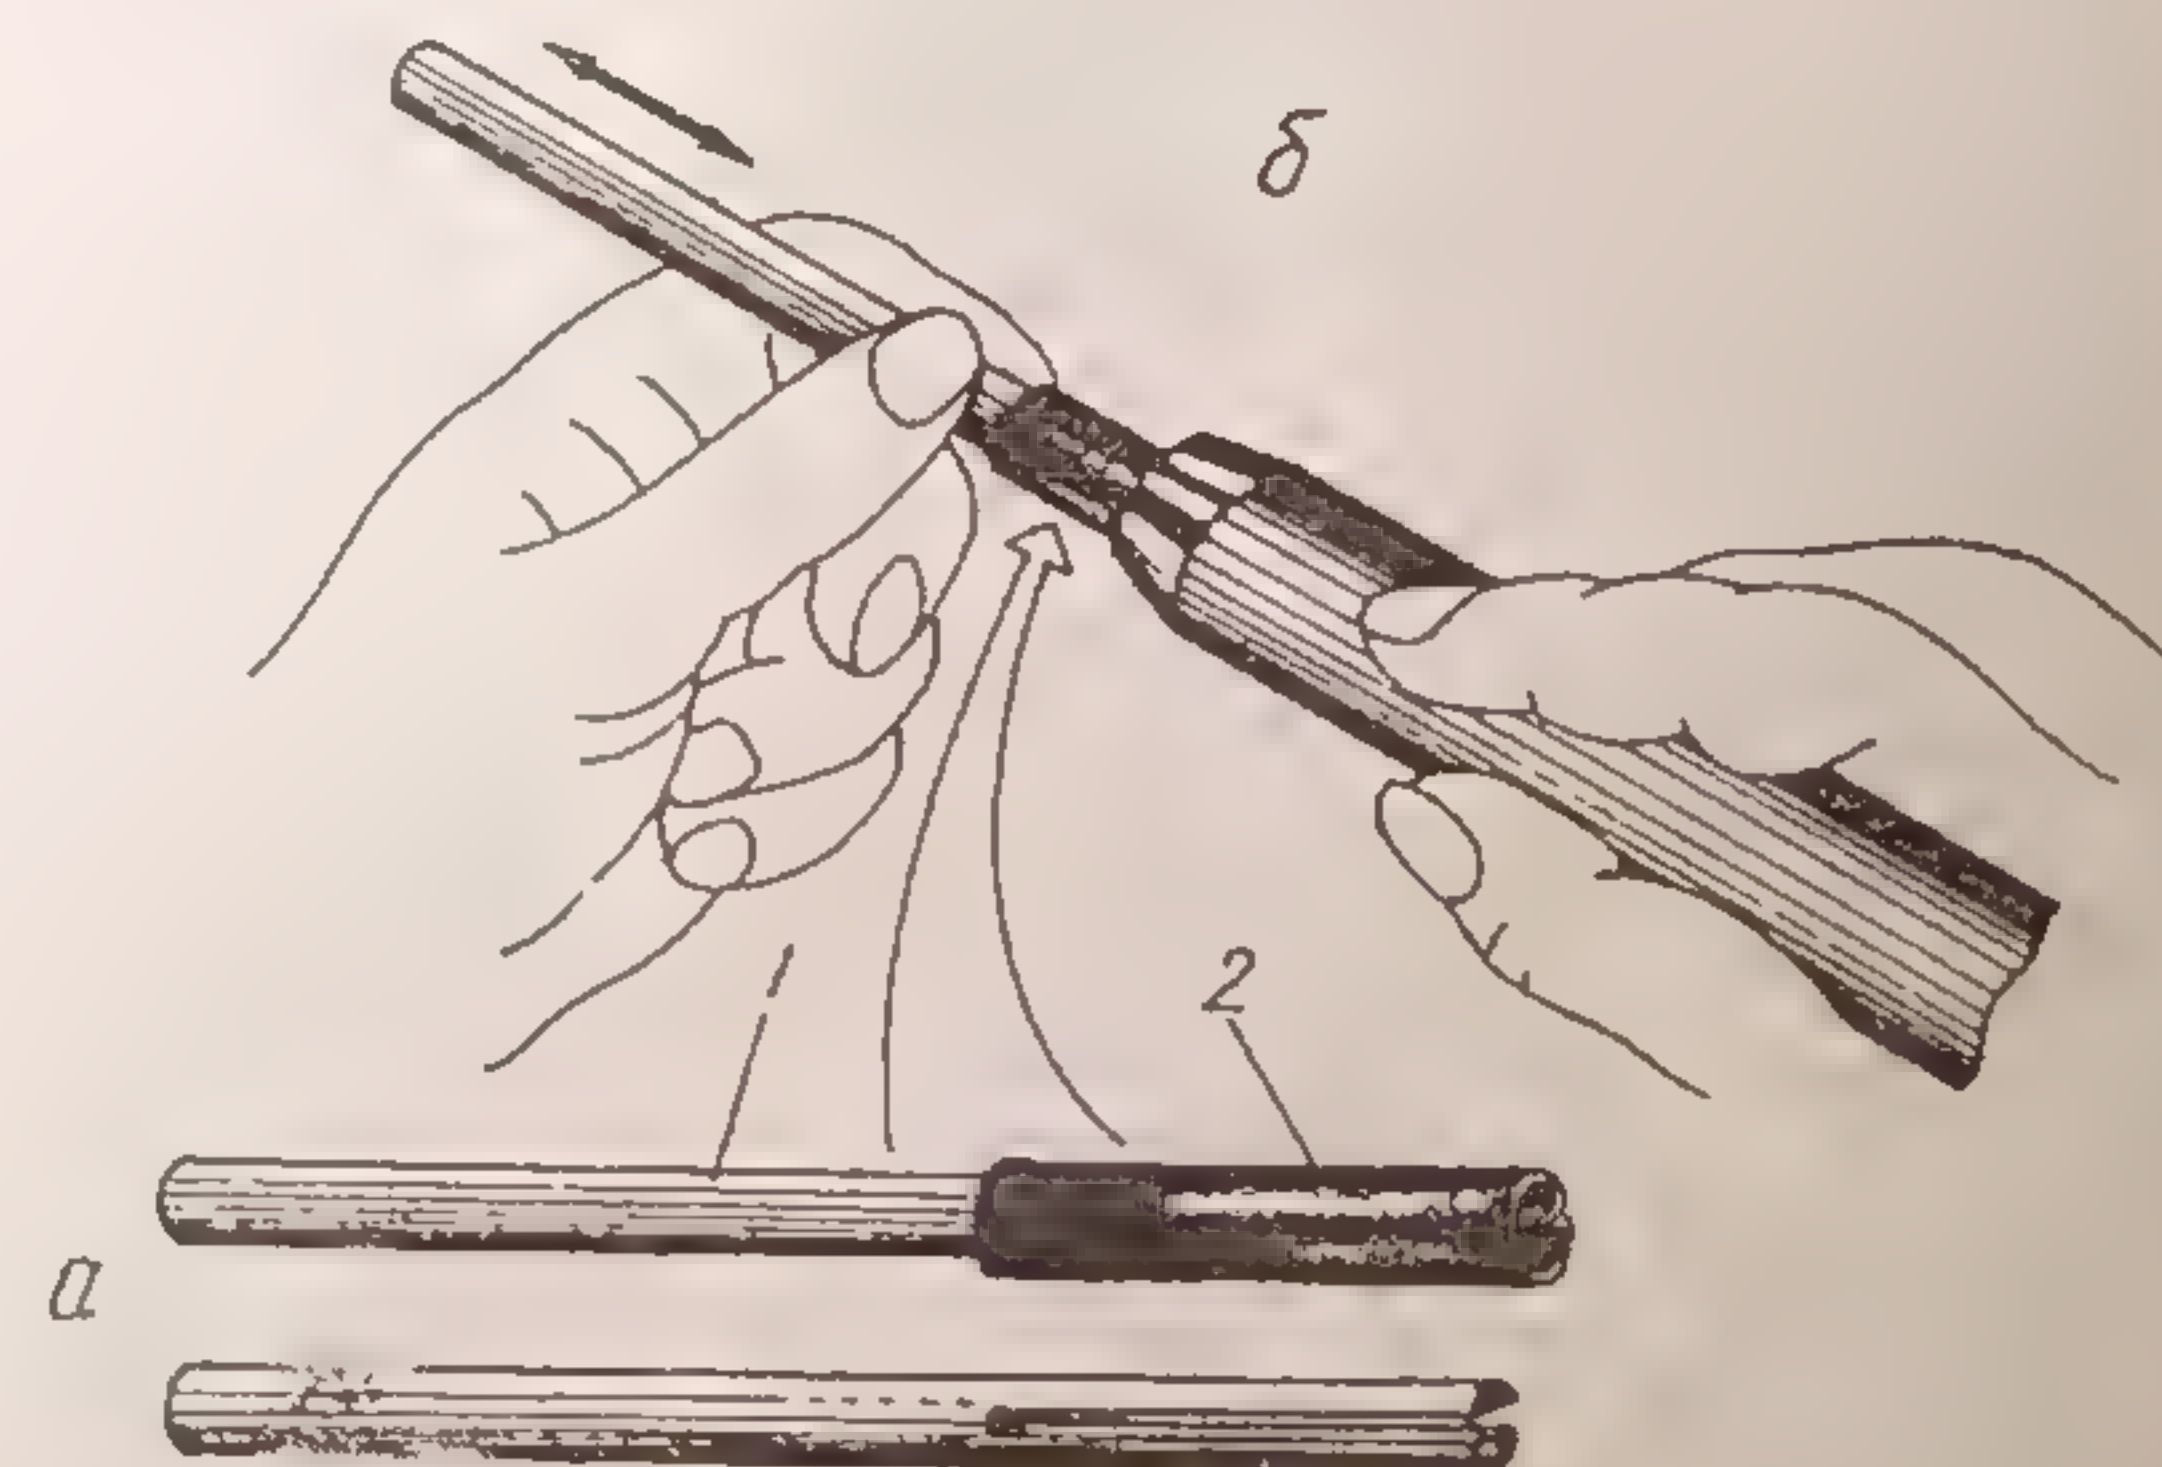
Прутки для правки внутренней части полукруглых резцов:
